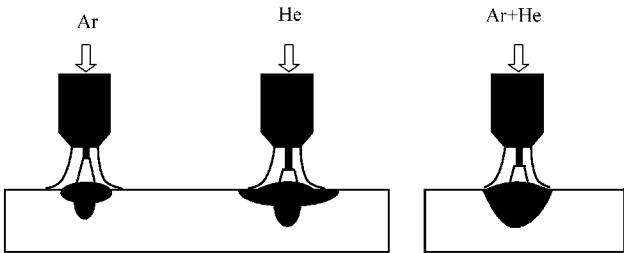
MIG 焊掺合氦气对焊缝成形的影响
